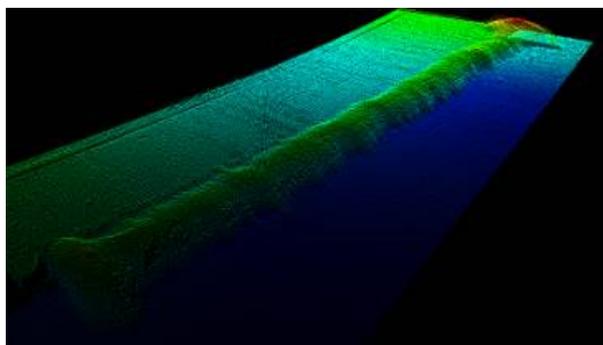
Exemplo de cordão de soldadura TWB laser com adição de fio após calibração do sistema
